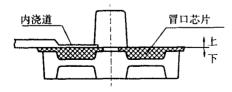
小齿轮两箱造型,—型多件工艺(湿型) Fig.9 Method for multi pieces of gear wheels per mould
